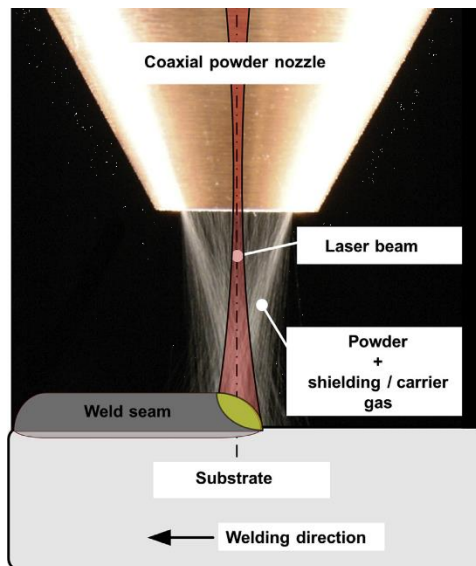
Processo de LASER cladding com visualização do bocal coaxial de uma LASER cladding head [30]
